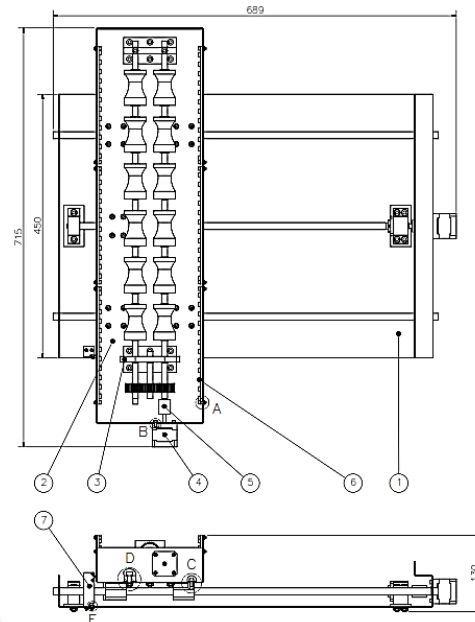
Mecanismo de rodillos - Plano PE1.2.1-A2
